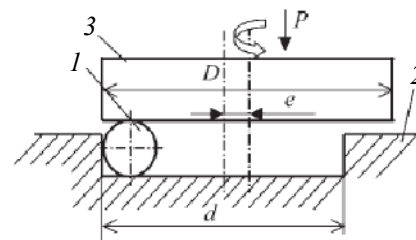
Схема накатывания сферической заготовки плоскими поверхностями:
